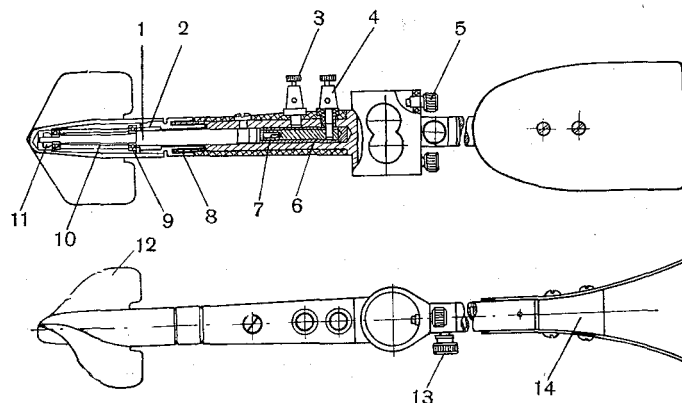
Устройство гидрометрической вертушки ГР-55.
